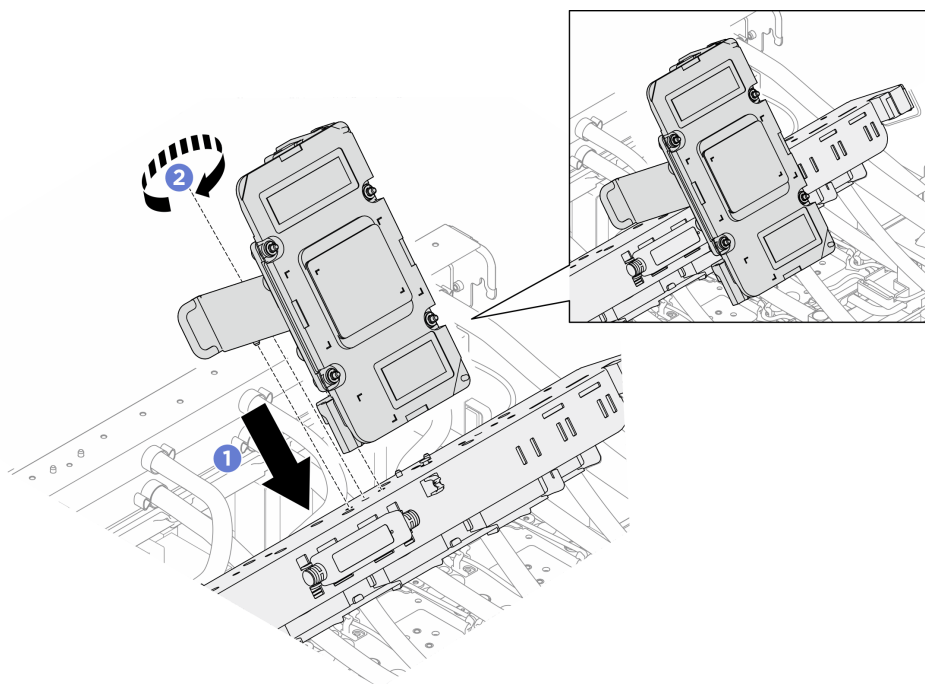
Installazione dell'assieme staffa di servizio e piastra a freddo della GPU
